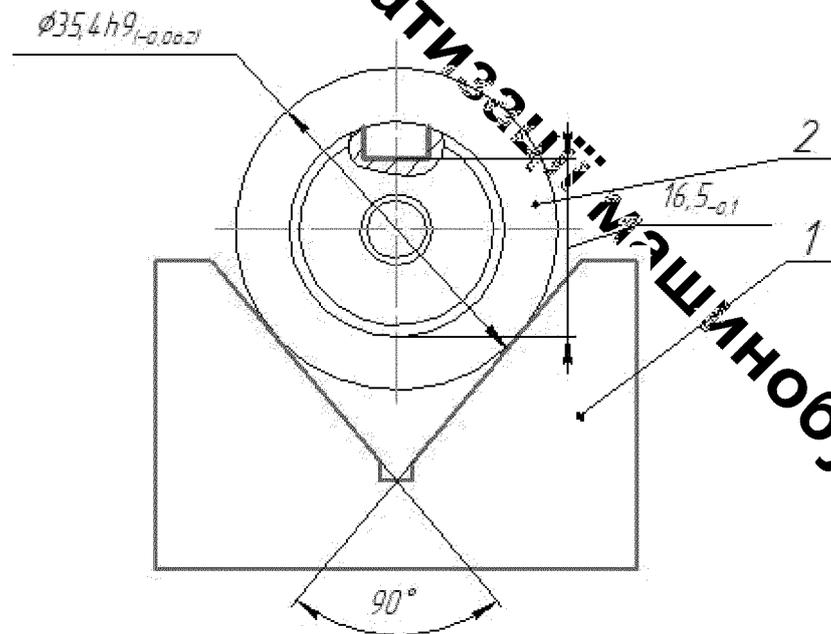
Реалізація схеми базування на розмір $16,5_{-0,1}$ мм, де 1 – призма; 2 –заготовка.
